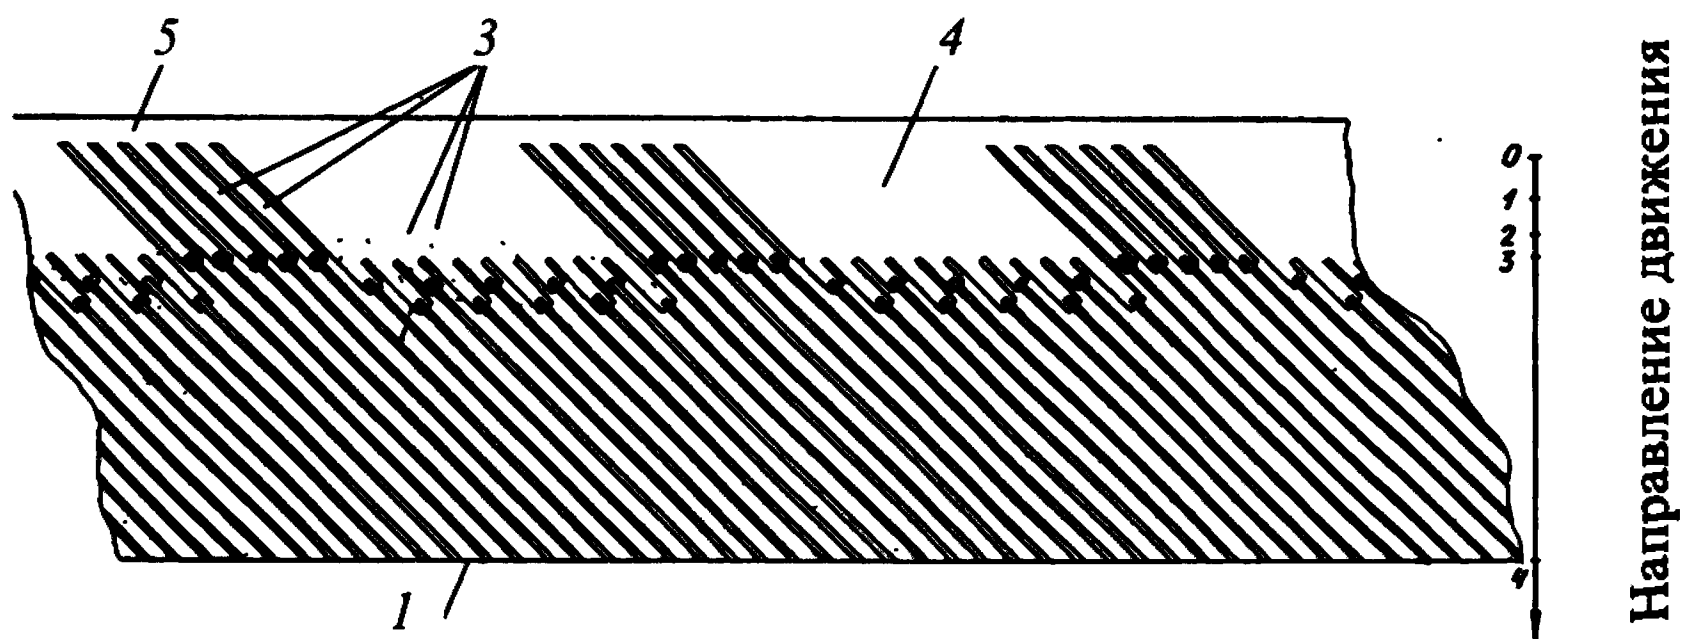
Развертка боковой внутренней цилиндрической поверхности стакана авторегулируемого УТГ
